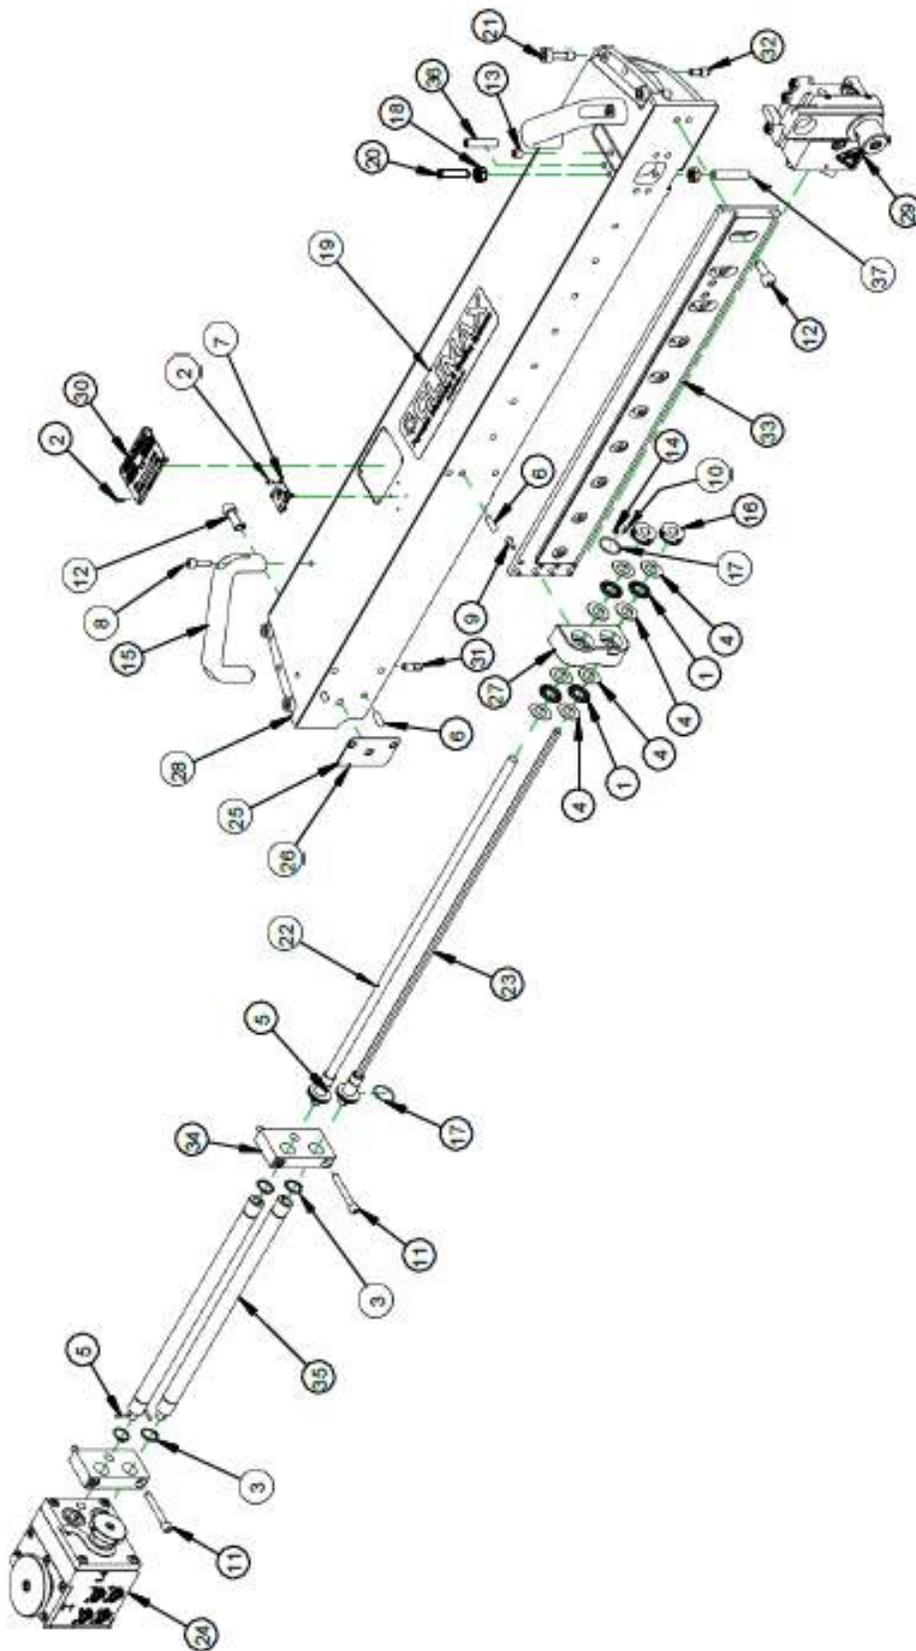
ENSEMBLE DE GLISSIÈRE RADIALE ET AXIALE FF3600 (RÉF. 80702)
